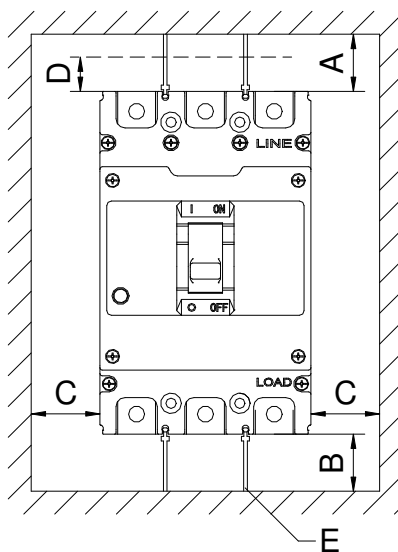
Габаритные и установочные размеры выключателей PRO.KVANT S1 типоразмера 1600
